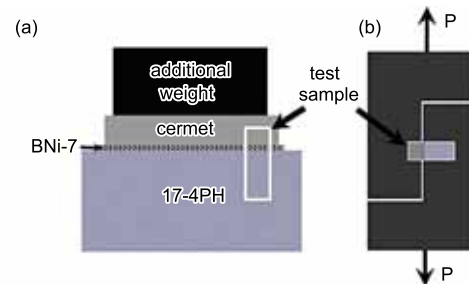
(a) 钎焊试片装配示意图; (b) 焊缝剪切实验工装
